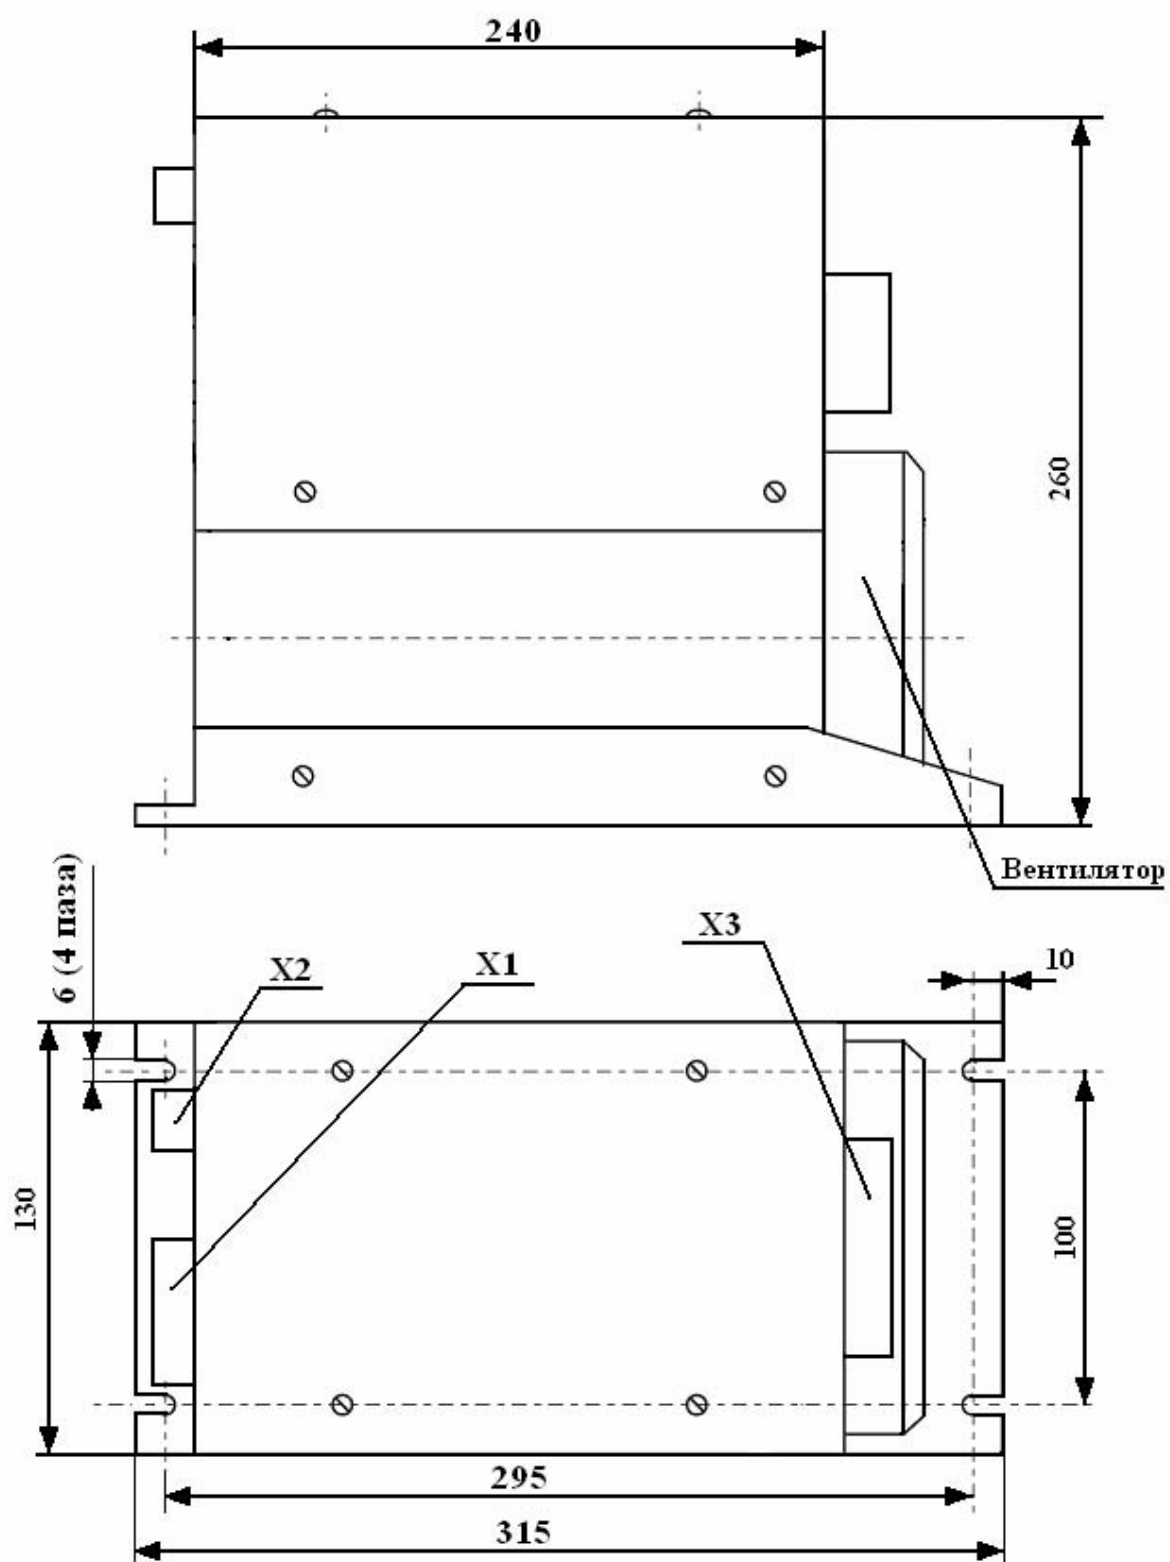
Габаритные размеры ПЕЛ-3-100-Е
